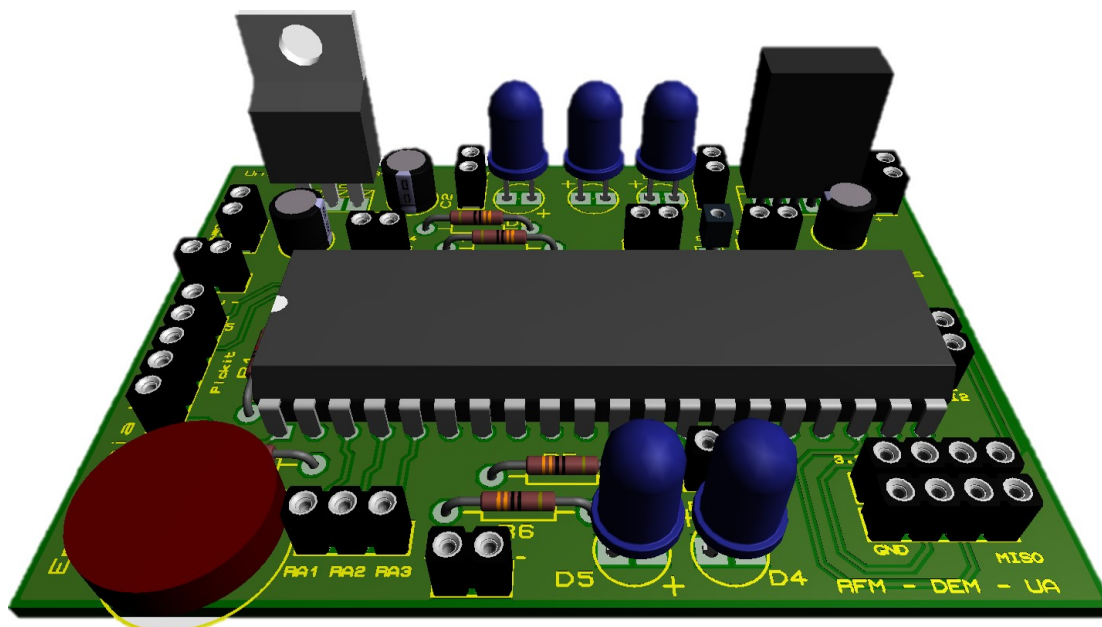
Desenho da PCB e componentes, em 3D - “Módulo habitáculo”
